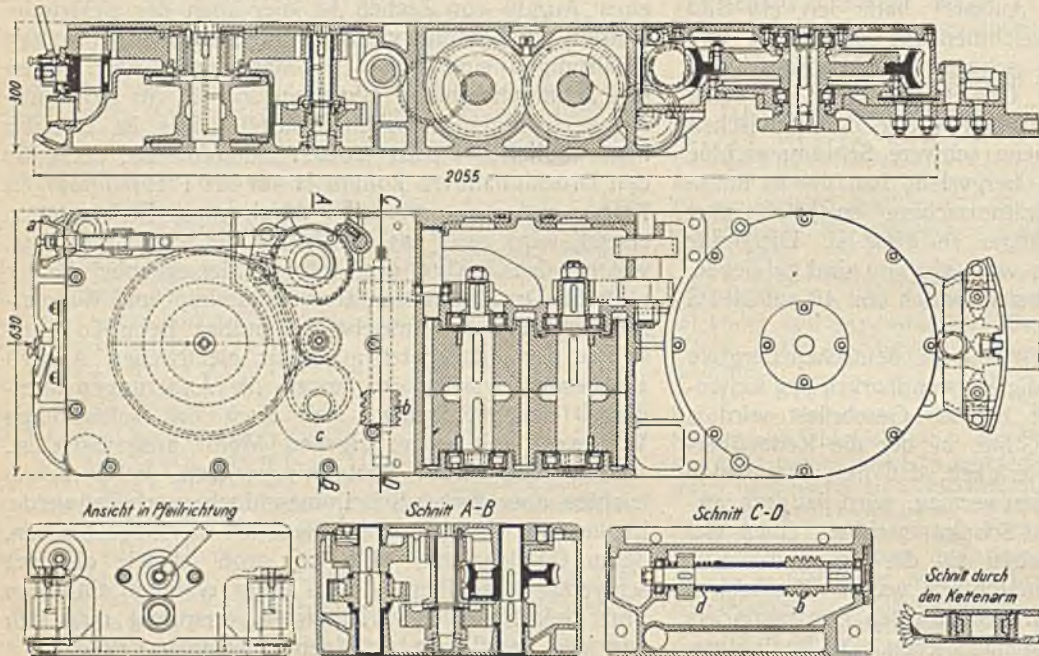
Leichte Kettenschrämmaschine der Maschinenfabrik Westfalia.
